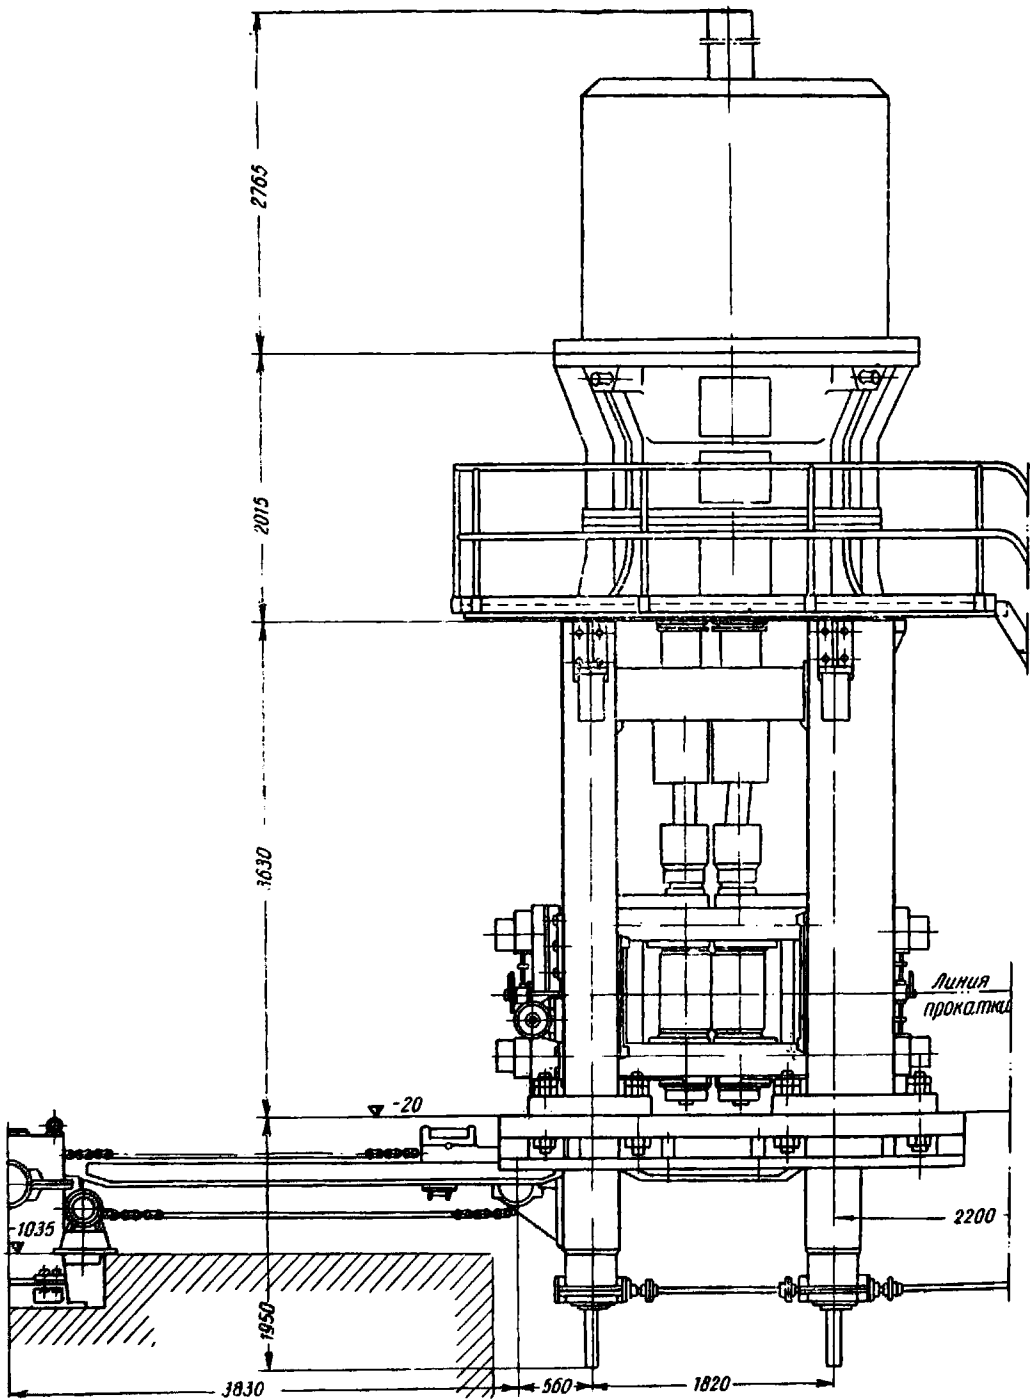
Рабочая клетка с вертикальными вальками сортового стана 350
